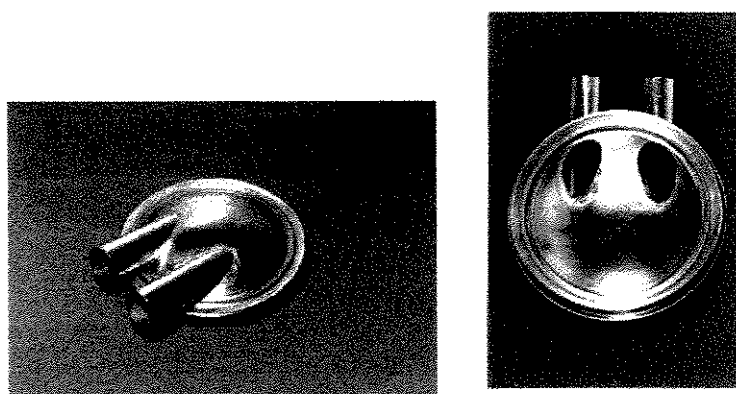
Carcaça superior de Ti soldada; (a) vista externa e (b) vista interna.
